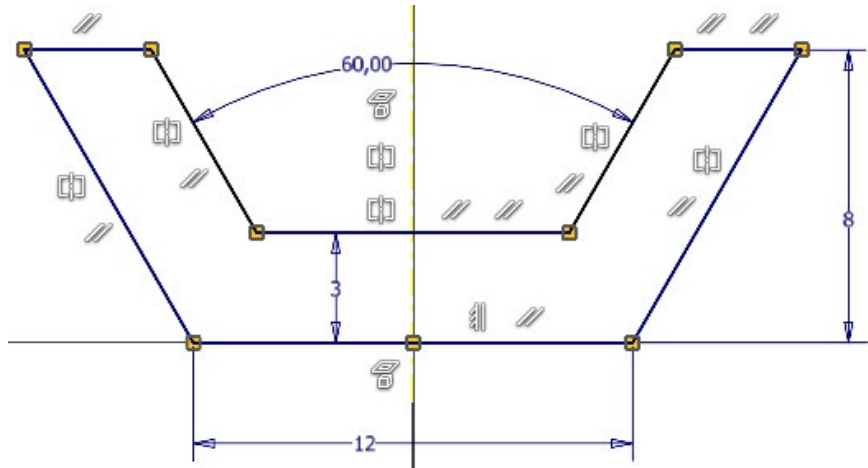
Boceto de la pieza con eje de simetría proyectado .
